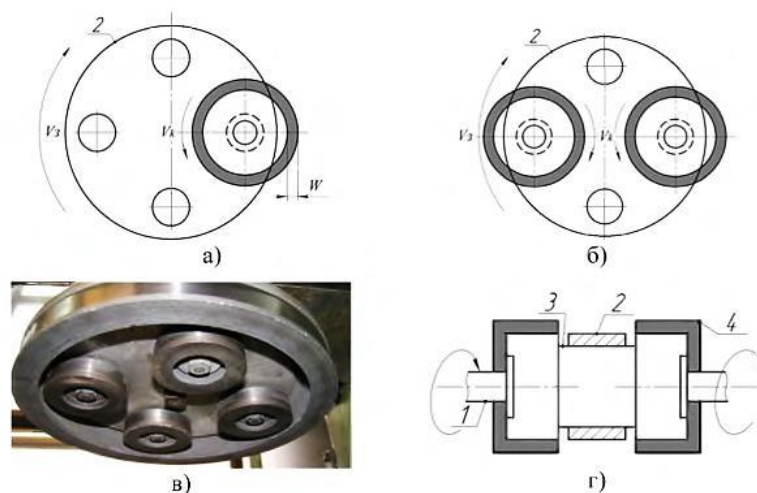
Разновидности схем плоской торцевой шлифовки: 1 – шпиндель; 2 – приспособление; 3 – заготовка; 4 – шлифовальный круг
